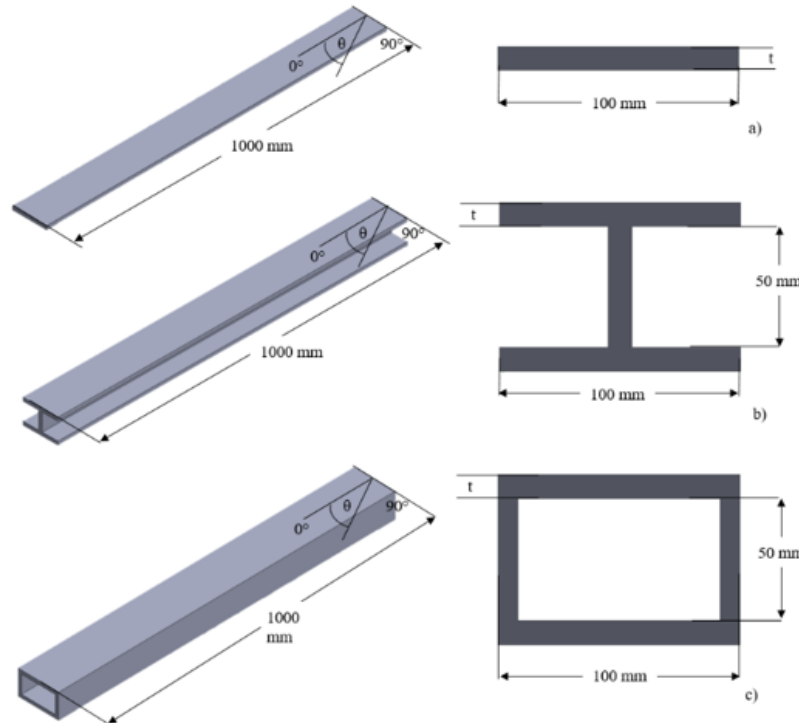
Vigas, (a) ST plana; (b) ST en I; (c) ST en caja.
